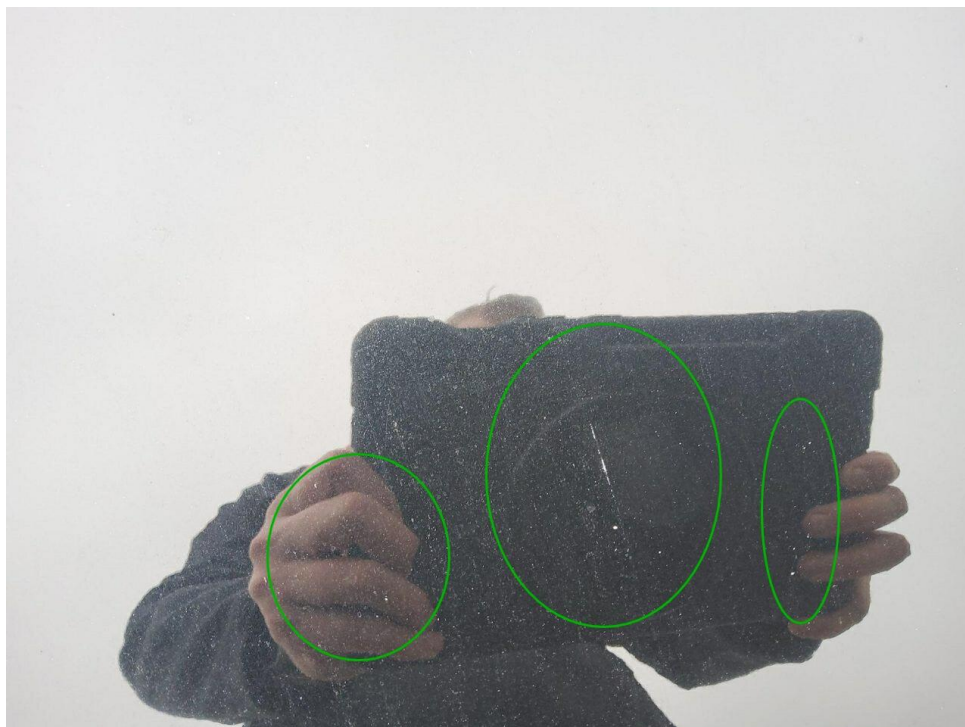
Motorhaube Lackierung, viele Steinschläge, lackieren mit Lackaufbau
